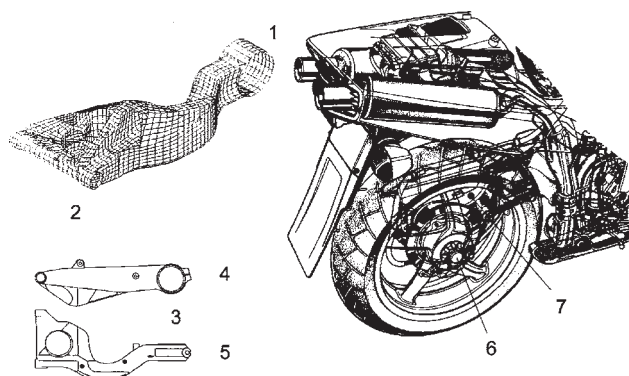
Systém zavěšení zadního kola Cantilever (Yamaha).
